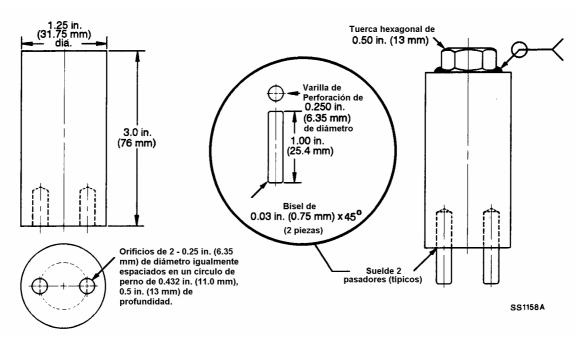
HERRAMIENTA SS1158 MONTAJE Y DESMONTAJE DEL TAPON
